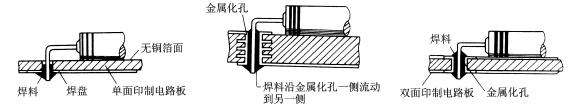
单面印制电路板上焊接 图 3.1.20 双面印制电路板上焊接 图 3.1.21 多层印制电路板上焊接 金属化孔双面印制电路板的焊接,按图 3.1.20 所示。焊接时采用单面焊接方法,使焊料在孔内充分润湿,并流向另一侧。如采用两面焊接,应充分加热,使孔内气体排出。
